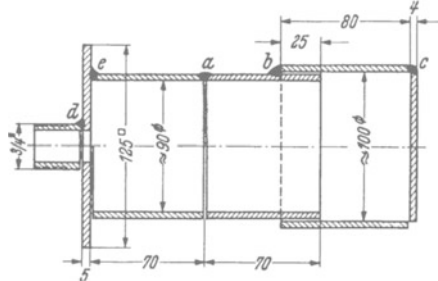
Geschweißter Rohrprüfkörper.
